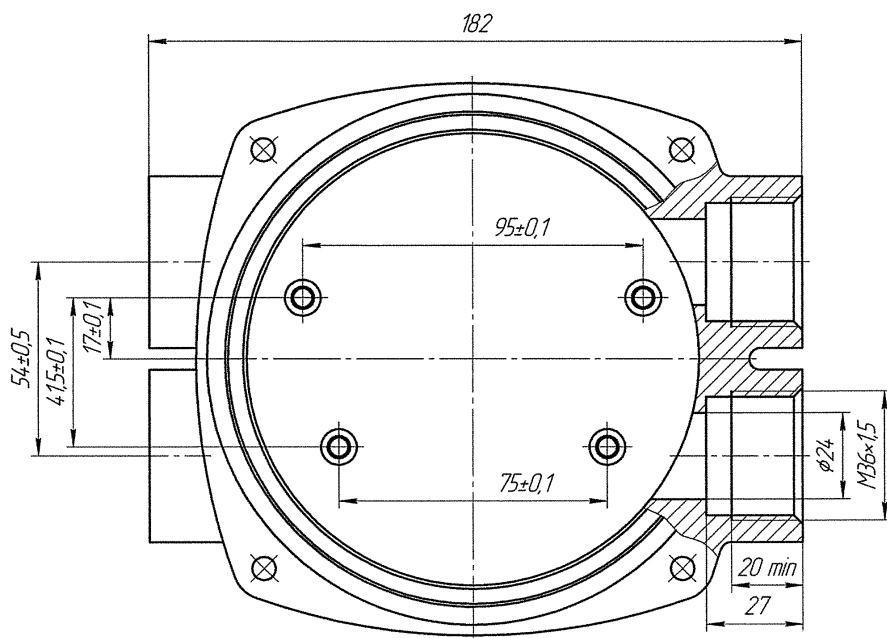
Габаритные и присоединительные размеры крышки соединителя в сборе
